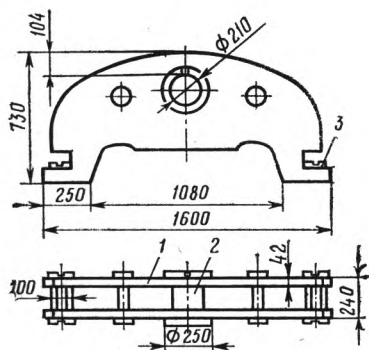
Чалочное приспособление для выемки и транспортировки дизеля тепловоза 2ТЭ10Л: 1 — щеки; 2 — валик; 3 — полублок
